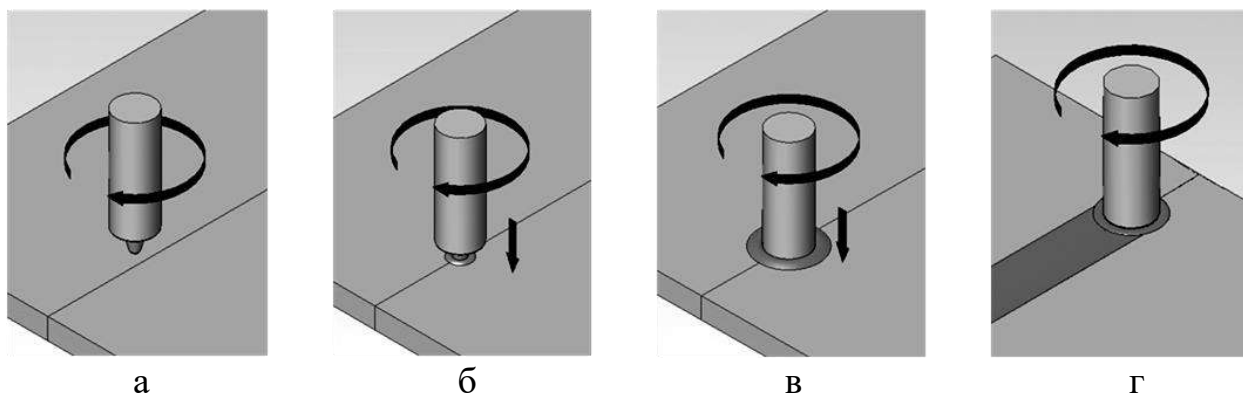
Стадии процесса сварки трением с перемешиванием: а – включение вращения инструмента; б – внедрение вращающегося инструмента в соединяемые заготовки; в – разогрев металла вокруг инструмента за счет сил трения; г – линейное перемещение вращающегося инструмента вдоль стыка заготовок
